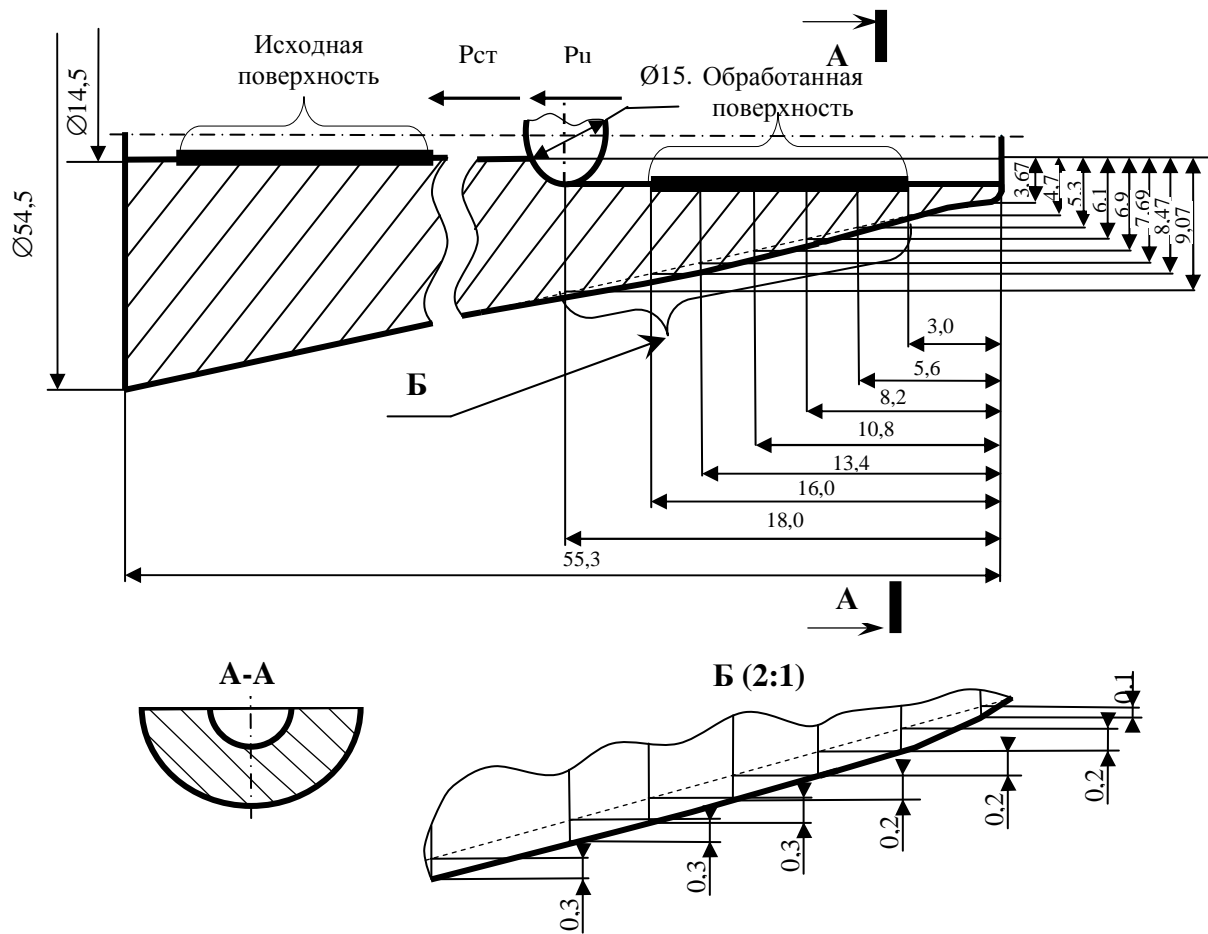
Схема обработки СИД образца имеющего форму усеченного конуса
